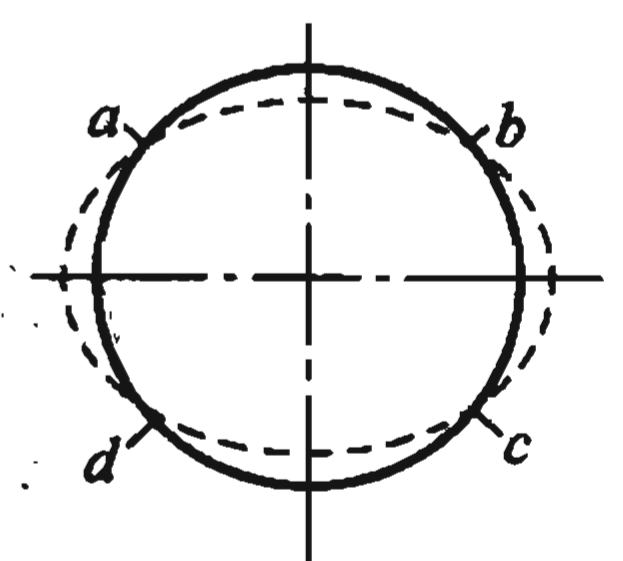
有缝钢管弯曲时焊缝的位置
